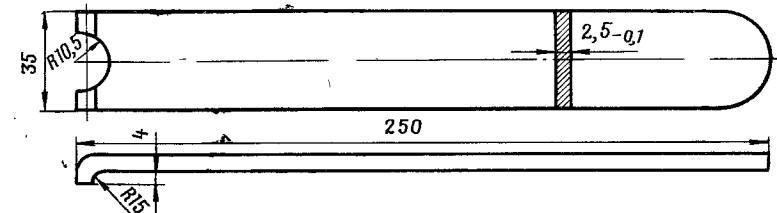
Ключ для гайки сальника штока цилиндра высокого давления
